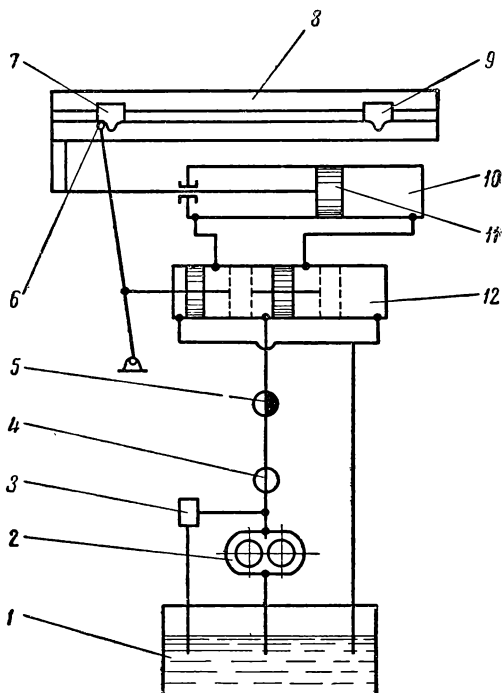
Схема гидропривода возвратно-поступательного движения стола
